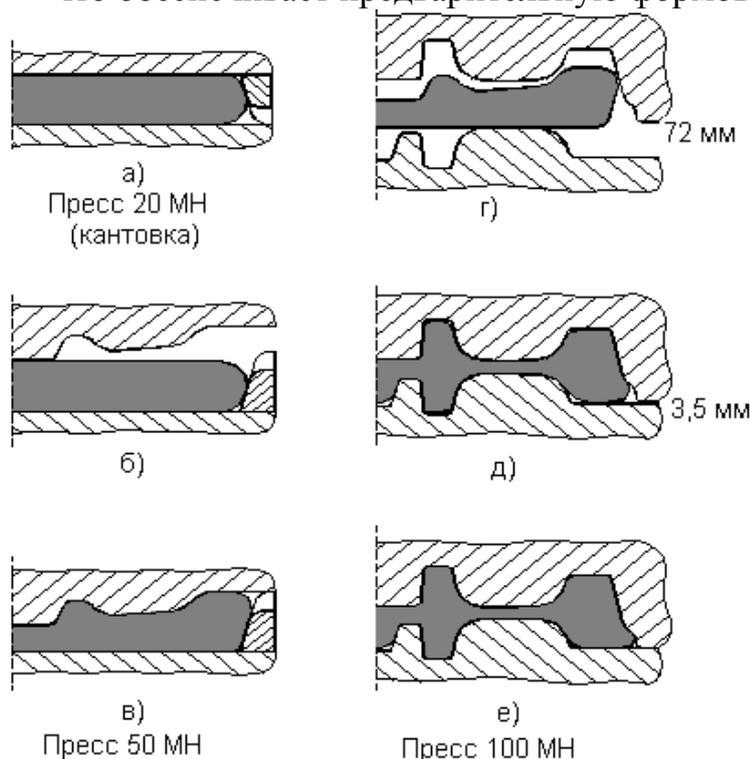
Технологическая схема штамповки колесных заготовок с гребнем $\varnothing 957$ мм.
